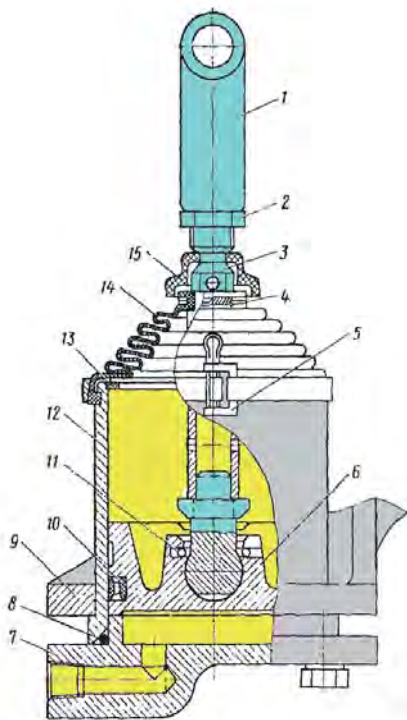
Цилиндр усилителя выключения сцепления: 1 - вилка; 2 - гайка; 3 - шток; 4 - шплинт-проволока; 5 - стяжная лента; 6 - поршень; 7 - крышка; 8 - уплотнительное кольцо; 9 - кронштейн; 10 - манжета; 11 - стопорное кольцо; 12 - корпус; 13 - кольцо; 14 - чехол; 15 - колпак фильтра
